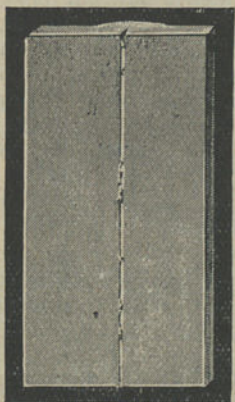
O avêso duma soldadura com falta de penetração.
